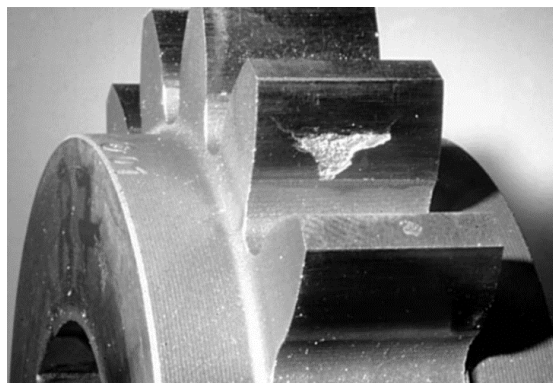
Fenómeno de picagem numa engrenagem de dentes retos [11]
